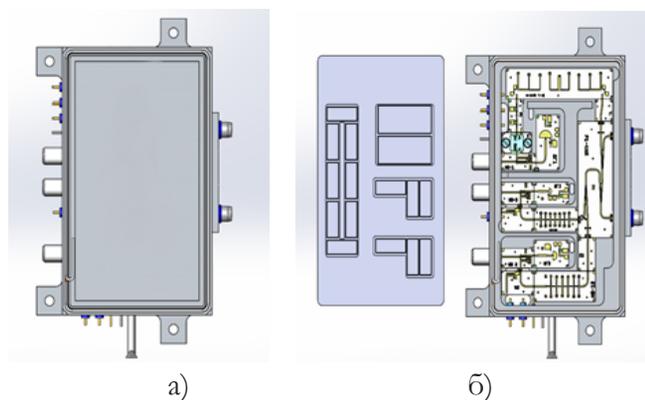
а) общий вид корпуса СВЧ диапазона, б) с радиочастотными поглотителями на крышке корпуса СВЧ диапазона.
